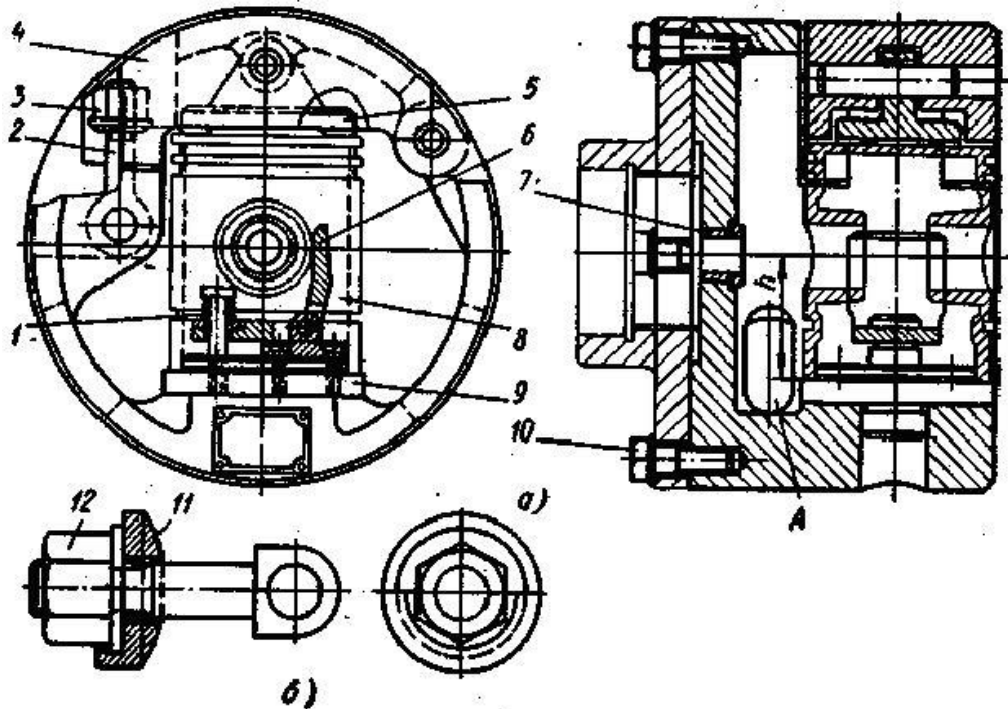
Пристрій для обробки отвору в поршні.
